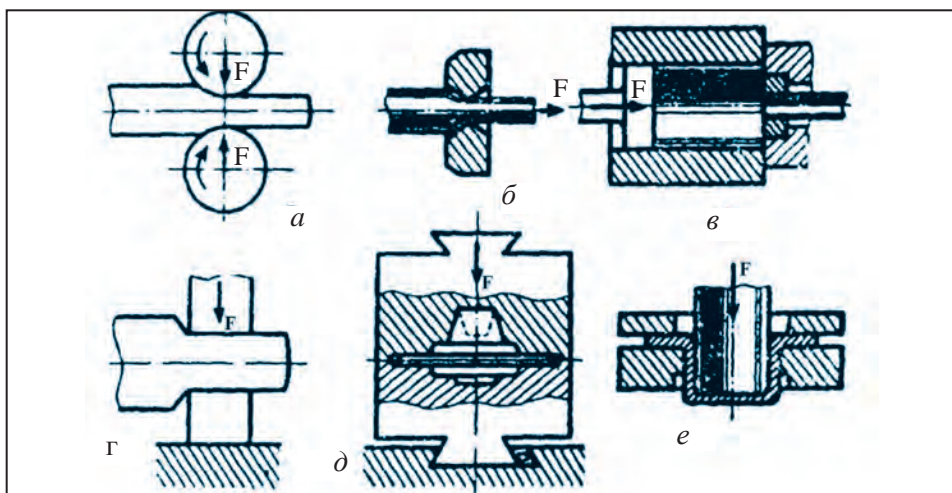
Обработка металлов под давлением: *а)* прокатка; *б)* волочение; *в)* прессование; *з)* ковка; *д)* горячая объёмная штамповка; *е)* холодная листовая штамповка.
